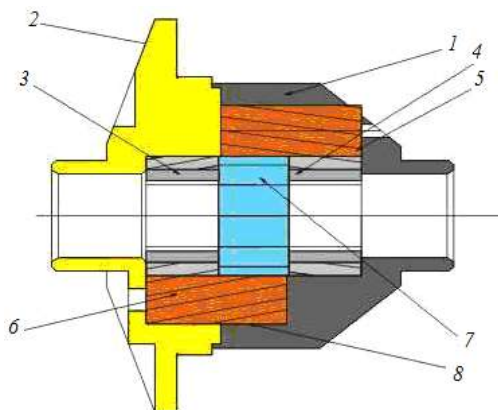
Ескіз диференціала Квайф: 1, 2 – корпус; 3, 4 – півосові шестерні; 5, 6 – сателіти; 7 – центральна шестерня; 8 – отвори (порожнини у збірному корпусі)
